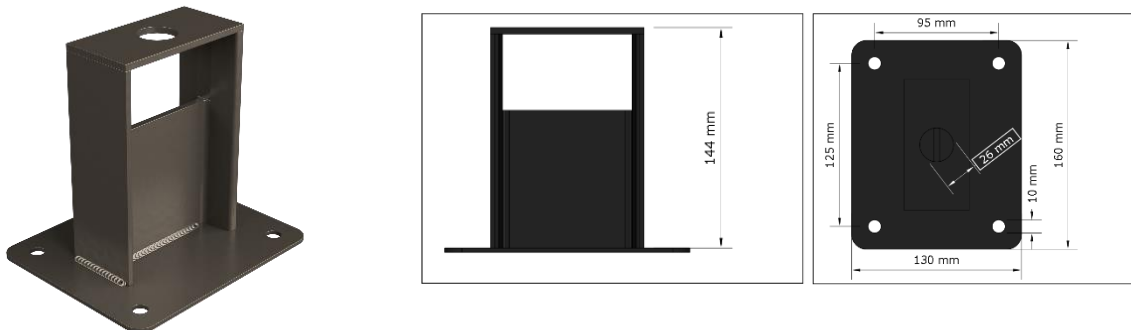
Apoyo aislado + planos frontal y superior. Fuente: Elaboración propia.
